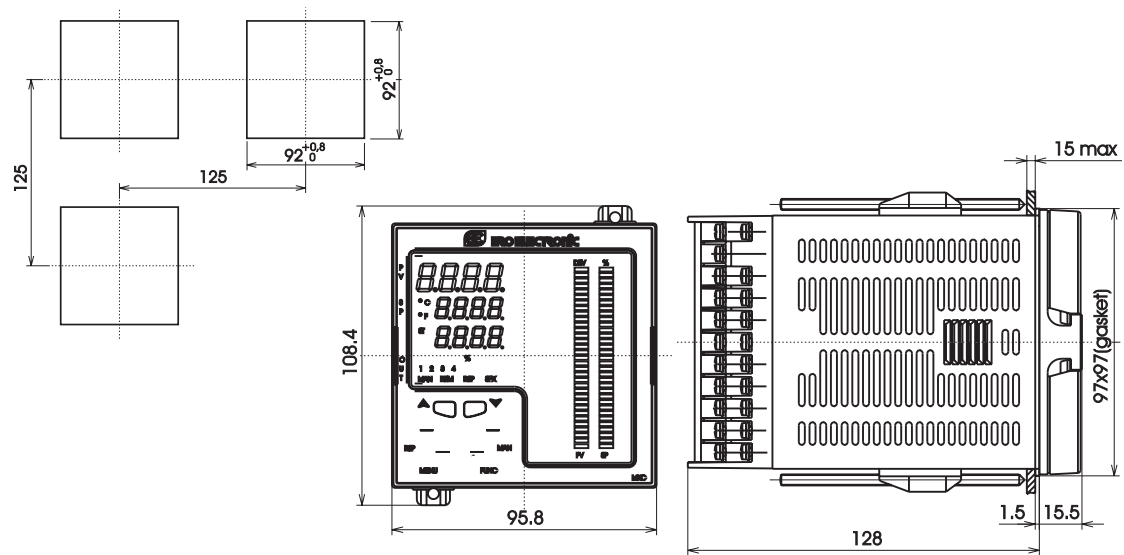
B DIMENSIONS ET PERCAGE POUR MKC
